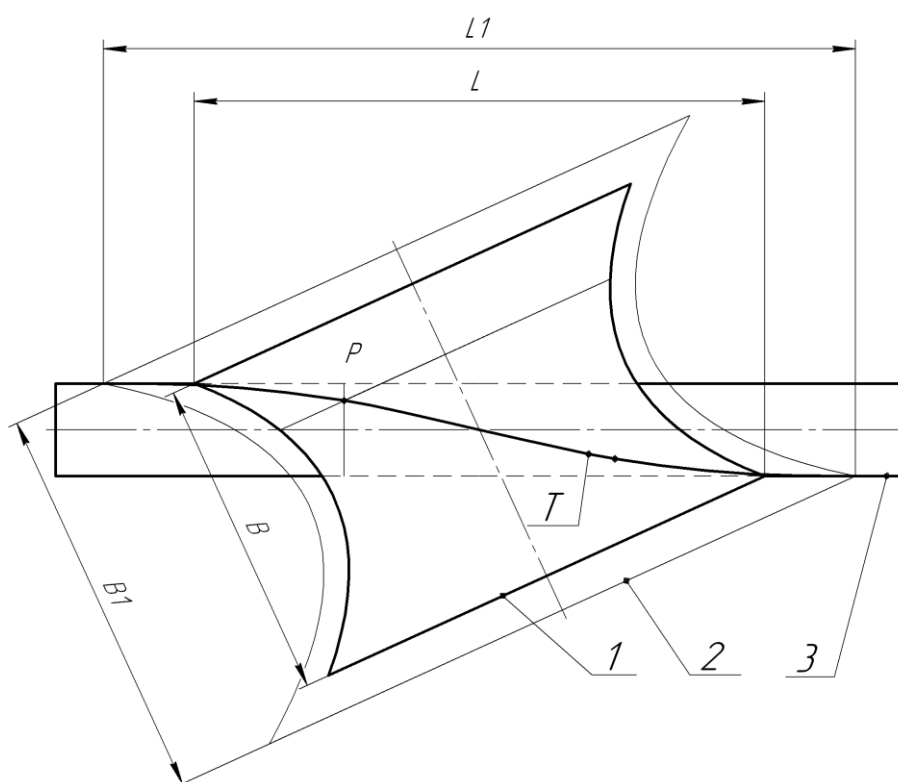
Линия контакта цилиндрического зубчатого колеса с глобоидным шлифовальным кругом: 1 – глобоидный шлифовальный круг высоты  $B$ ;
